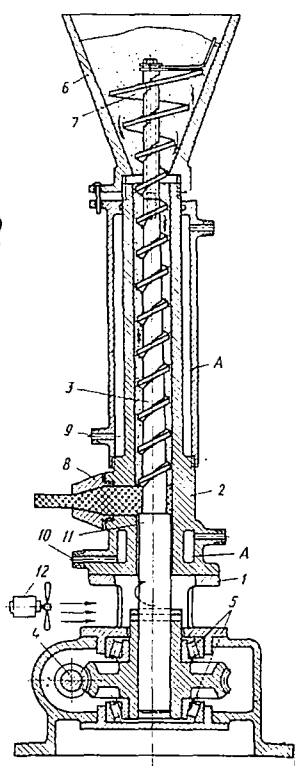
Вертикальный червячный пресс с верхней загрузкой
